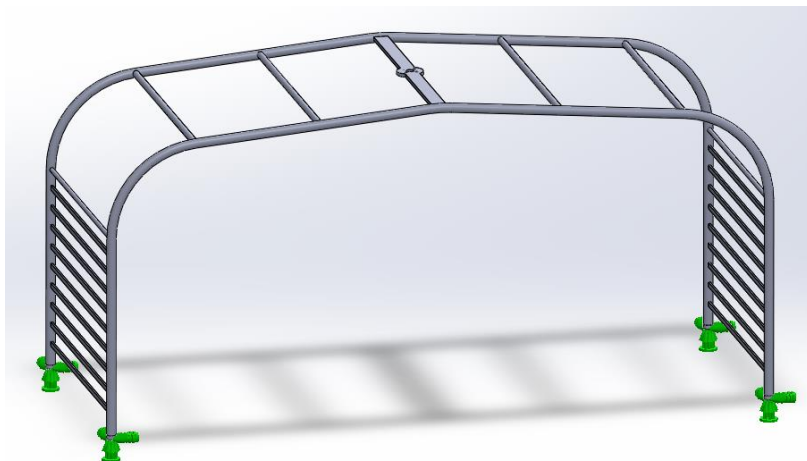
Vista de las sujeciones para el cálculo de la estructura. Fuente: Propia.
